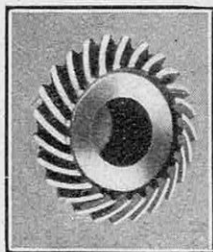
ENGRENAGE CONIQUE DE FORME SPIRALE TERMINÉ
